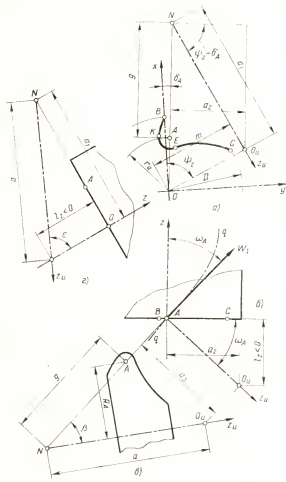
Схема для расчета параметров установки дисковой фрезы для обработки винтовой канавки цилиндрической фрезой
